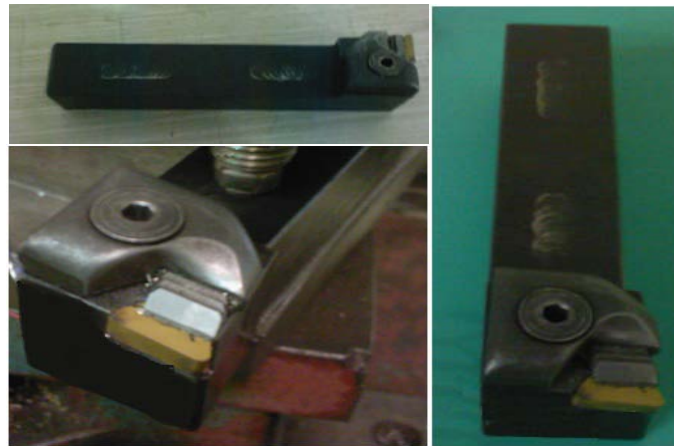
Outil de coupe, porte outil à plaquettes amovibles, utilisé lors des essais d'usinage
